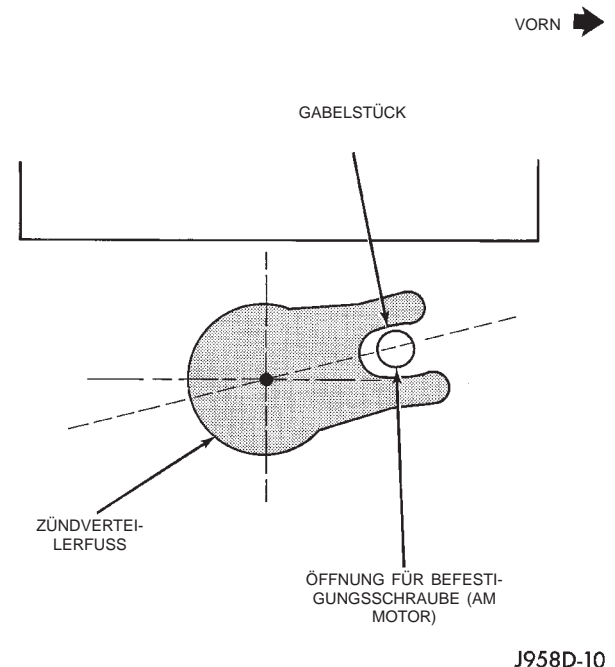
Einbaulage des Zündverteilers—4.0L-Sechszylindermotor
